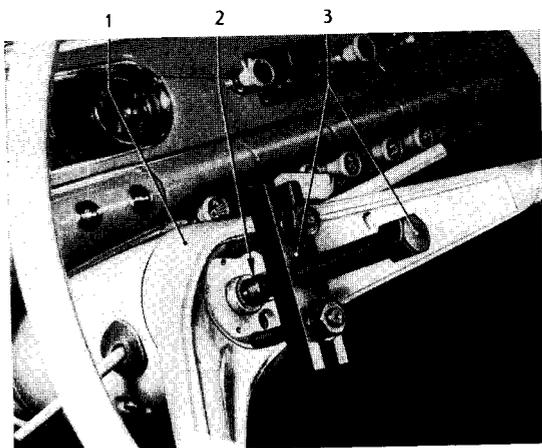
Lenkrad mit Spezial-Werkzeug abziehen
